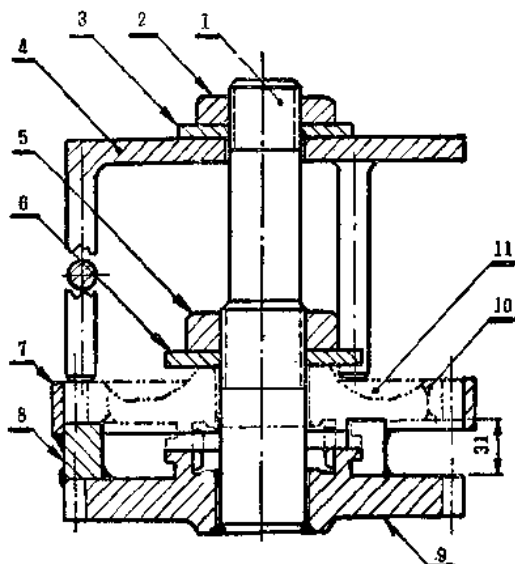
压合和焊接齿轮芯部和齿环用的压具
